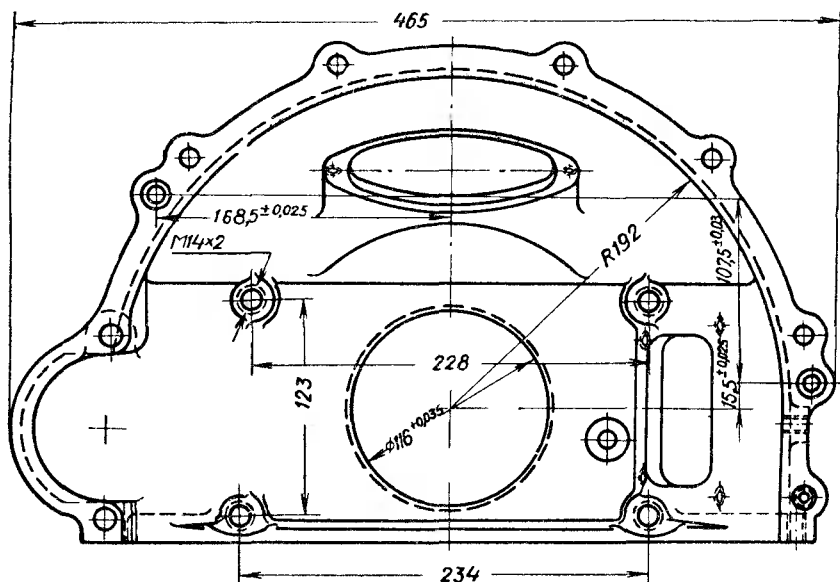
Картер сцепления двигателя ЗМЗ-53
